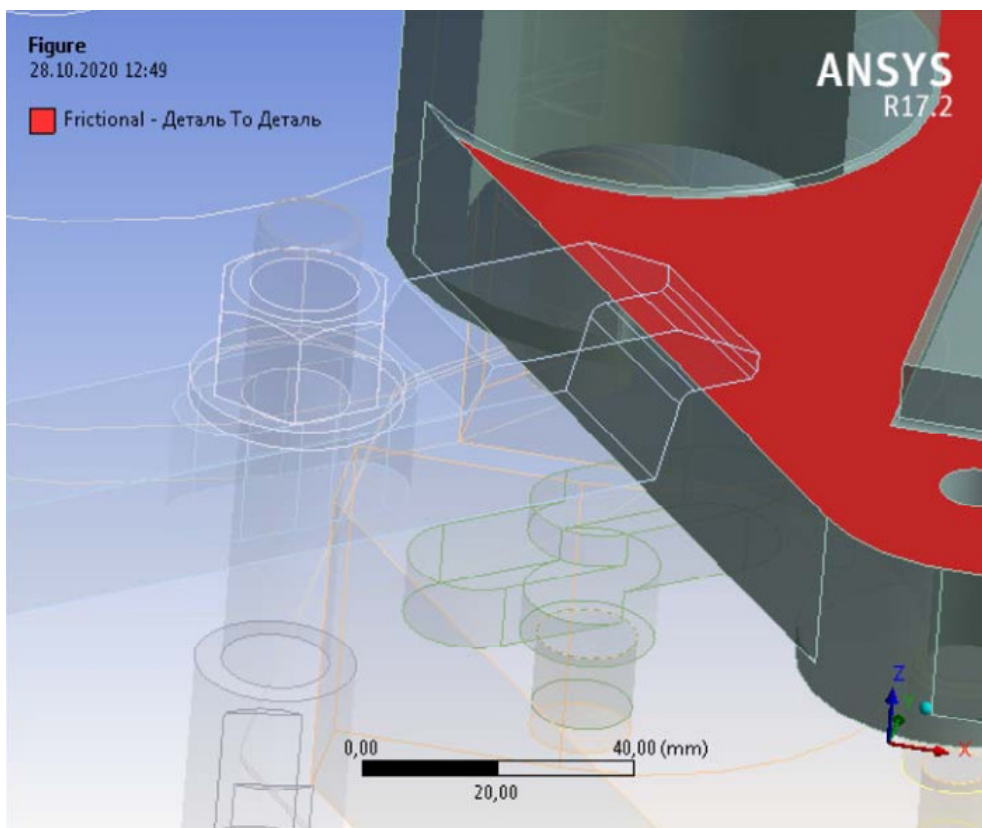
Зв'язок типу «тертя» між прихватом та заготовкою
